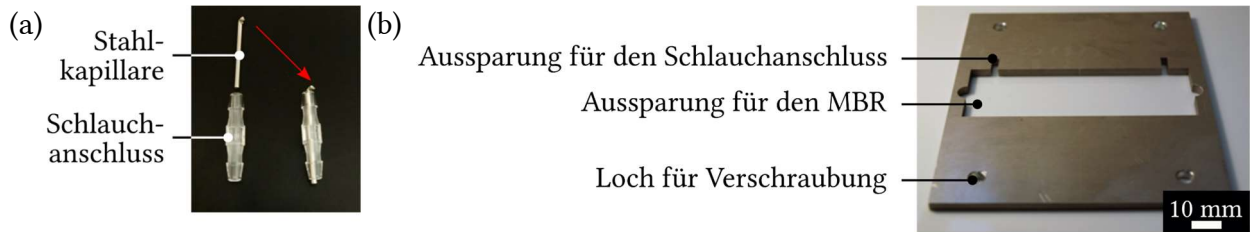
Vorbereitung für das Ultraschallschweißen der Chiphälften und der Schlauchanschlüsse. (a) Einstecken von Stahlkapillaren in die Schlauchanschlüsse vor dem Ultraschallschweißen, (b) Halterung zum Ultraschallschweißen, hier am Beispiel des 800 μl -MBR.
